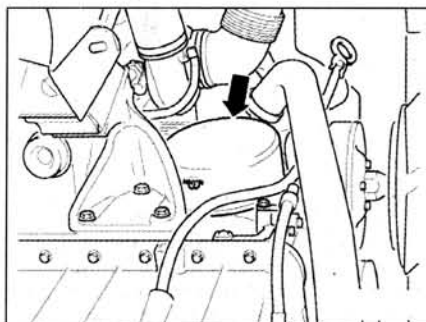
Расположение масляного фильтра двигателей AGK и ATA.
